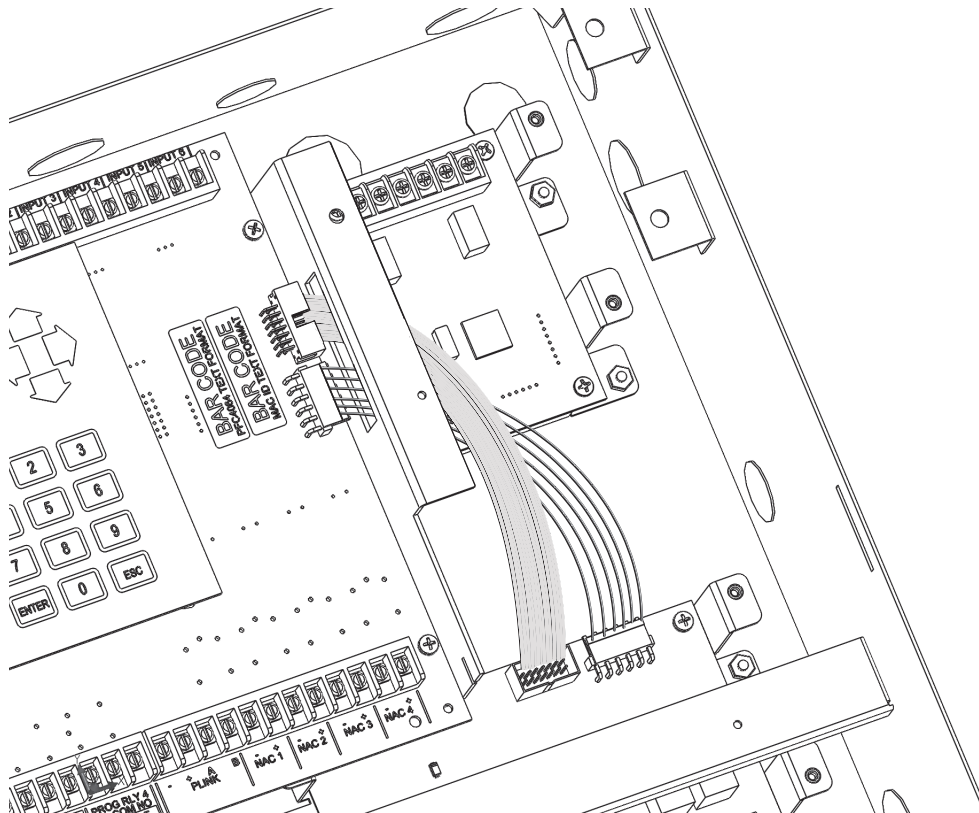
Exemplo de módulo CA-4064 instalado atrás da PCA principal
